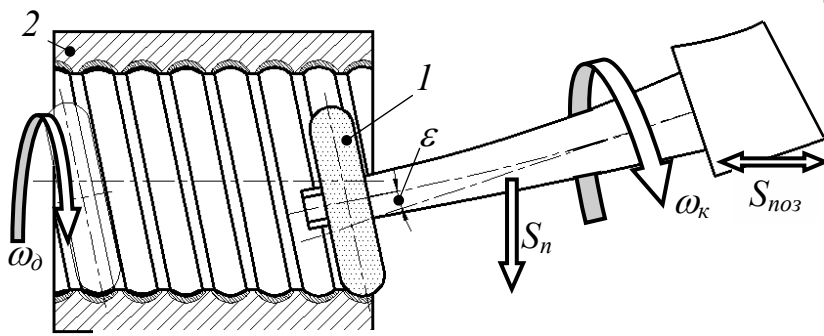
Загальна схема багатопрохідного шліфування гвинтової канавки
